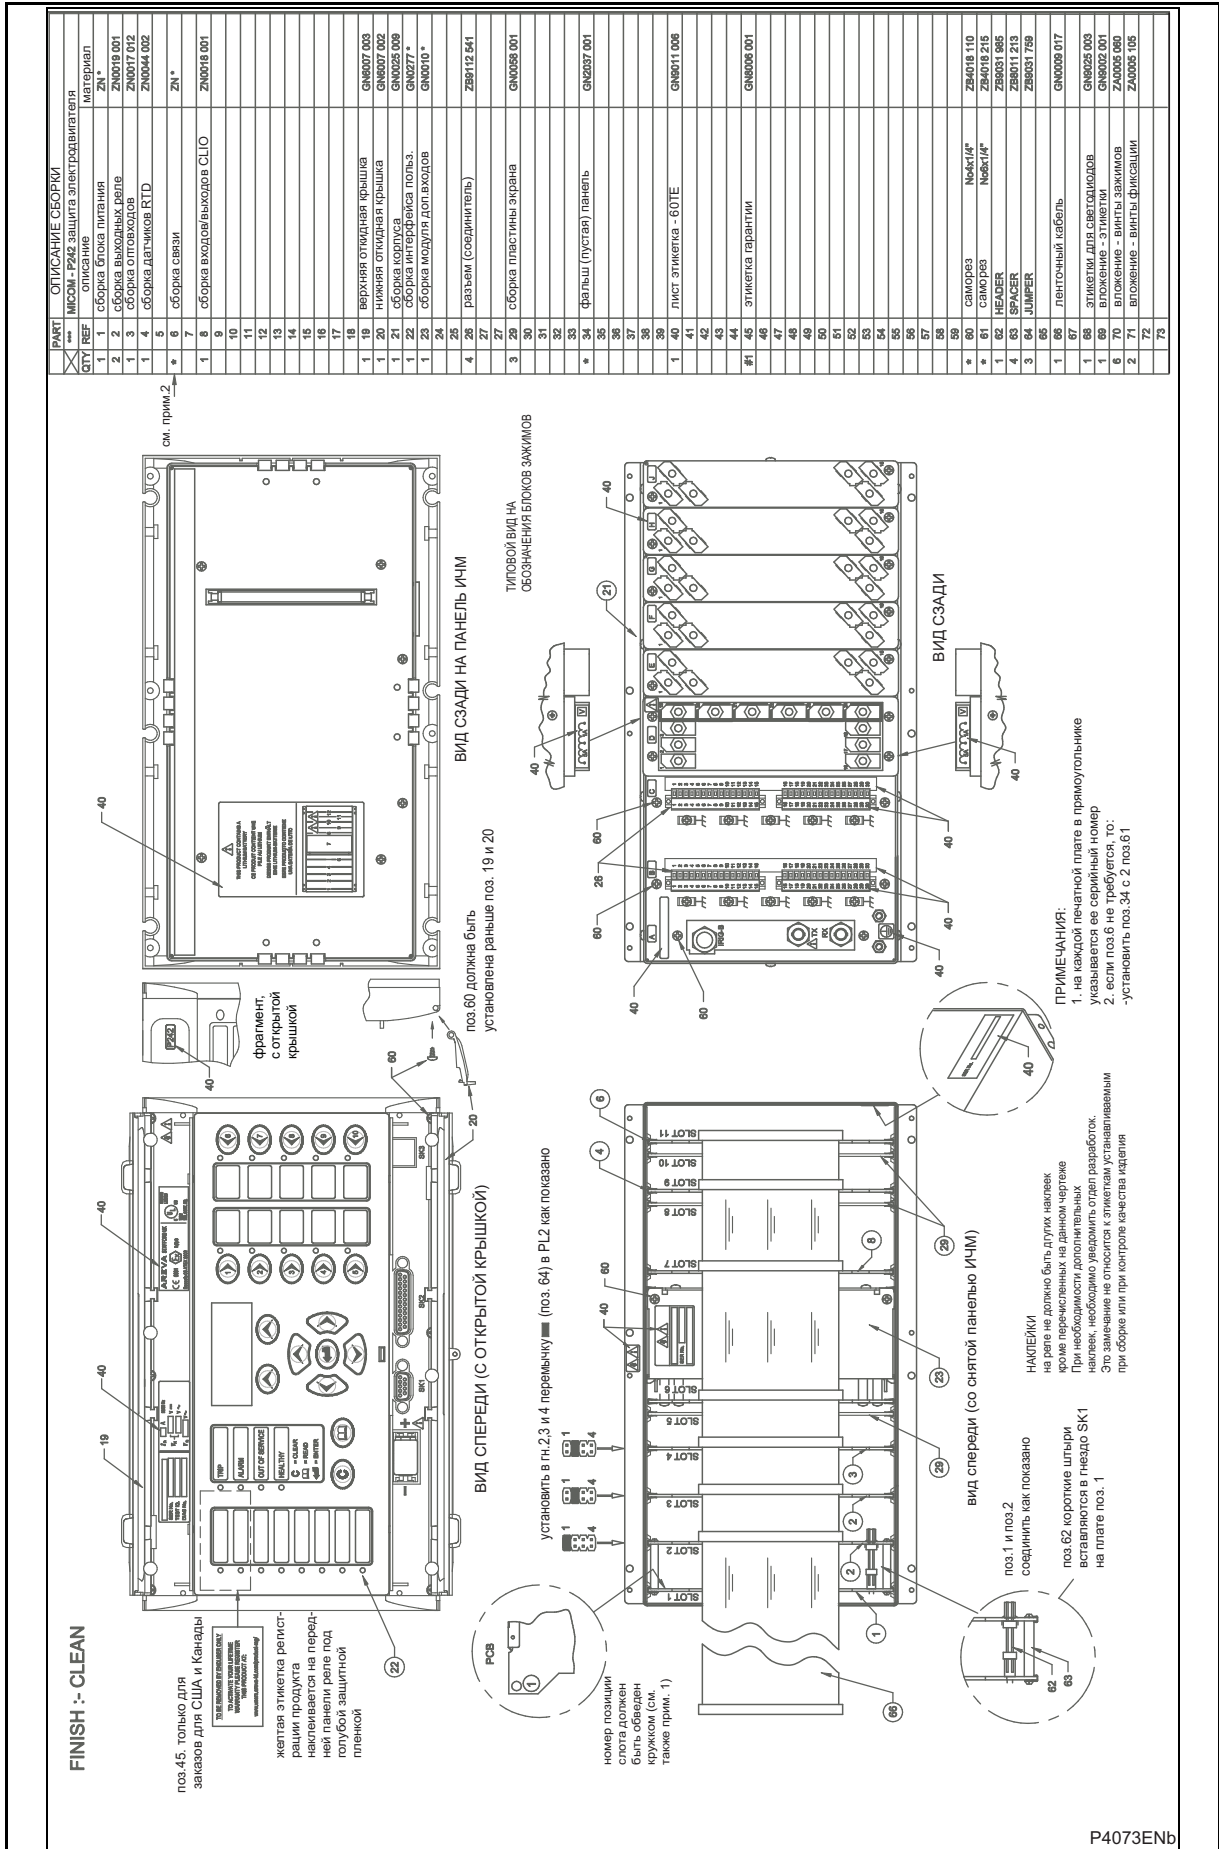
Сборочный чертеж реле защиты двигателя P242 (60TE) (16 входов и 16 выходов с дополнительными датчиками RTD и CLIO)
